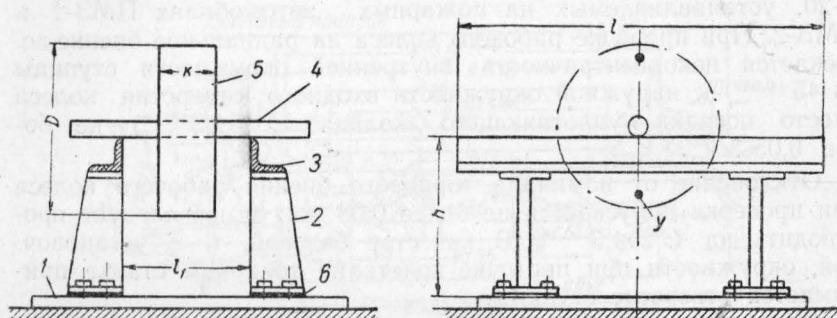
Схема стэнда для статической балансировки вала насоса и рабочего колеса:
